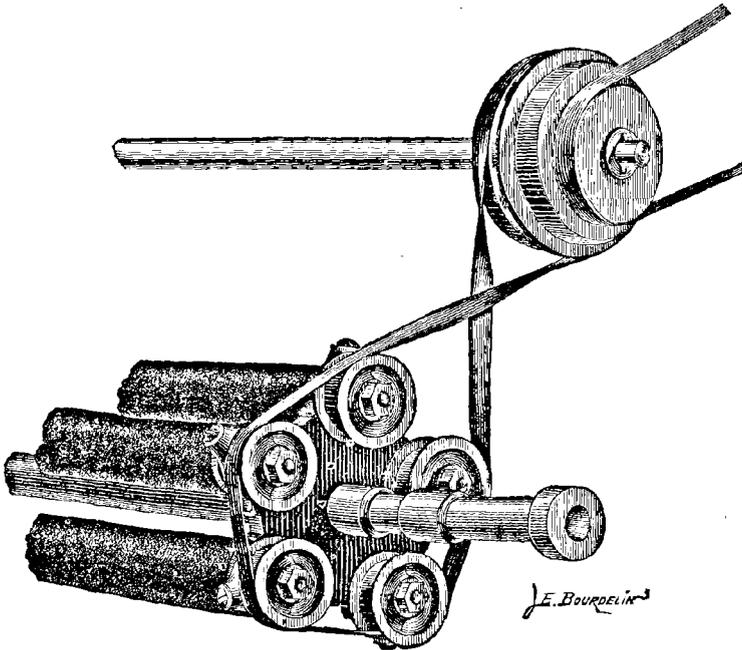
Disposition d'une extrémité du tambour laineur de la machine Grosselin.
